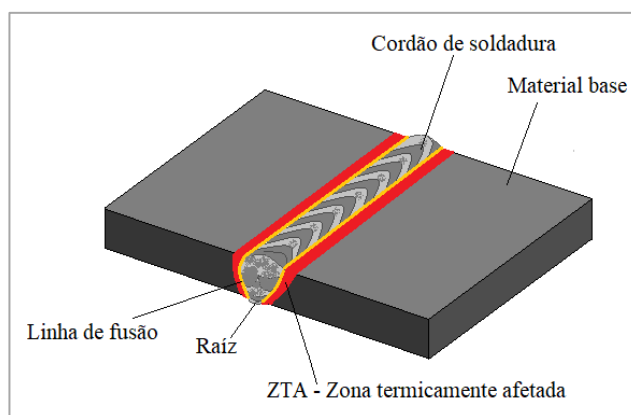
Principais regiões de uma soldadura – [3] Imagem adaptada
